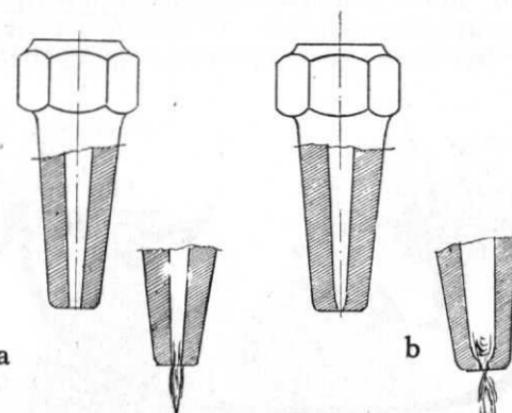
Víceplamenové svářecí hořáky ke svářecím strojům.
